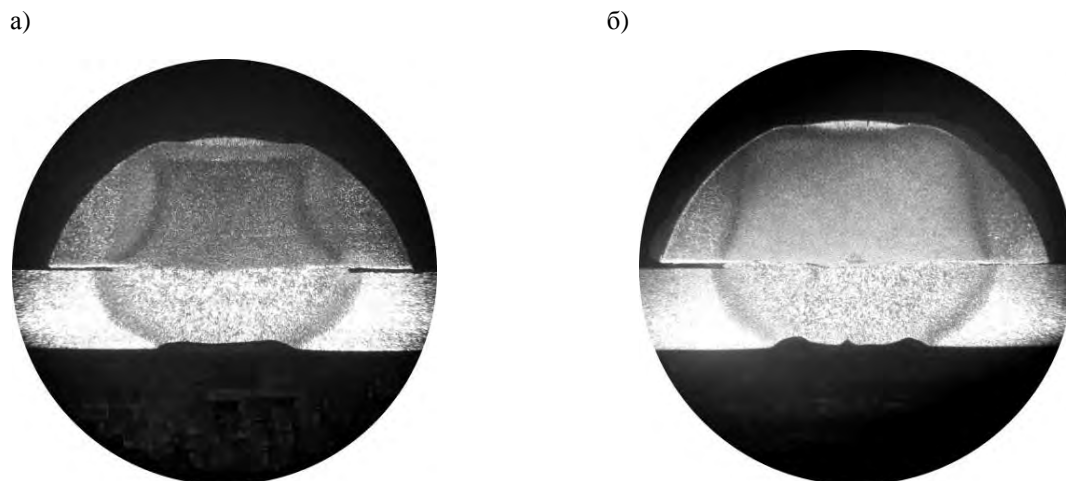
Макрошлифы сварных соединений засова: а – при сварке на расчетных режимах; б – при сварке с использованием системы автоматического управления процессом КРС
